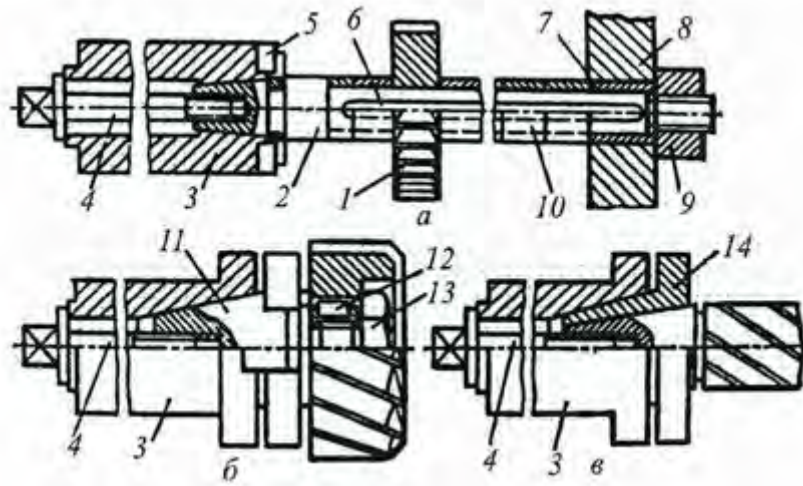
Способи закріплення інструменту на фрезерних верстатах
